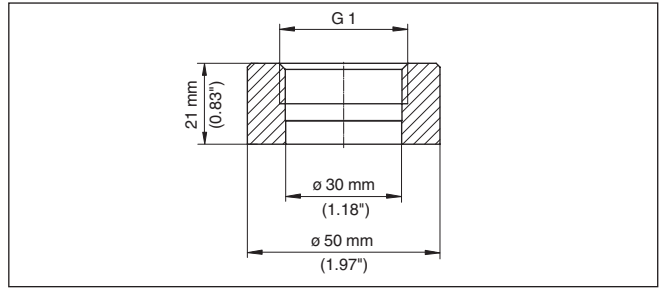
Maße Einschweißstutzen G1 (ISO 228-1)
